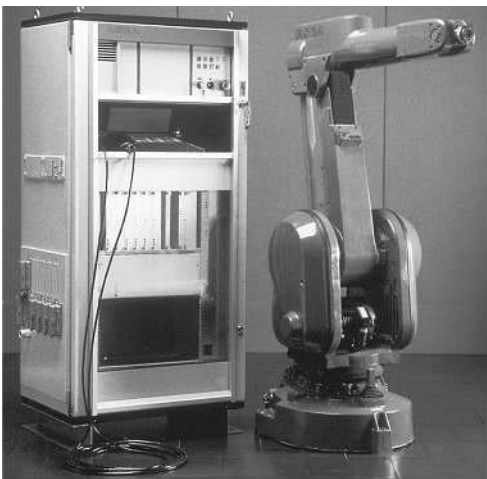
6-achsiger Roboter mit Steuerschrank (Quelle: ABB)
